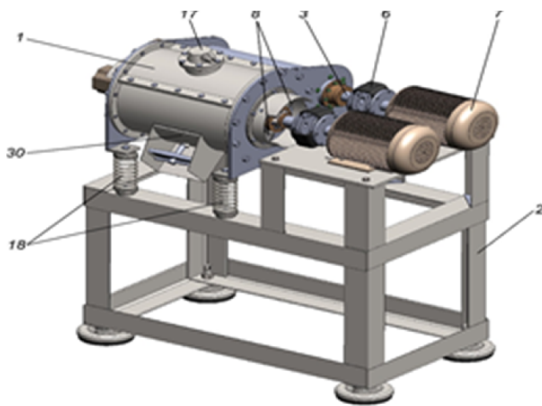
Вибрационная машина для отделочно-упрочняющей обработки деталей [3]
